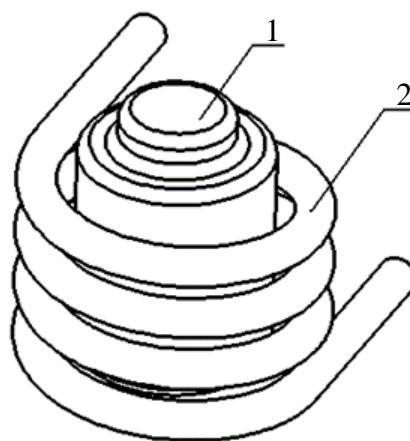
Витковой индуктор с ферритным сердечником:
